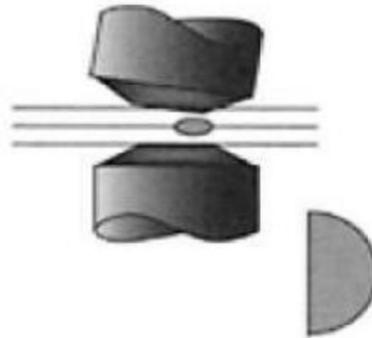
c: Punto de soldadura producido por electrodos desalineados angularmente.
